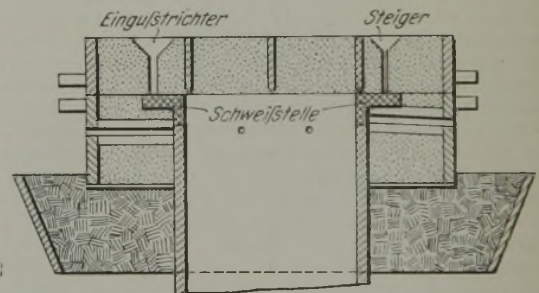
Einbau des Gußstückes zum Schweißen.
